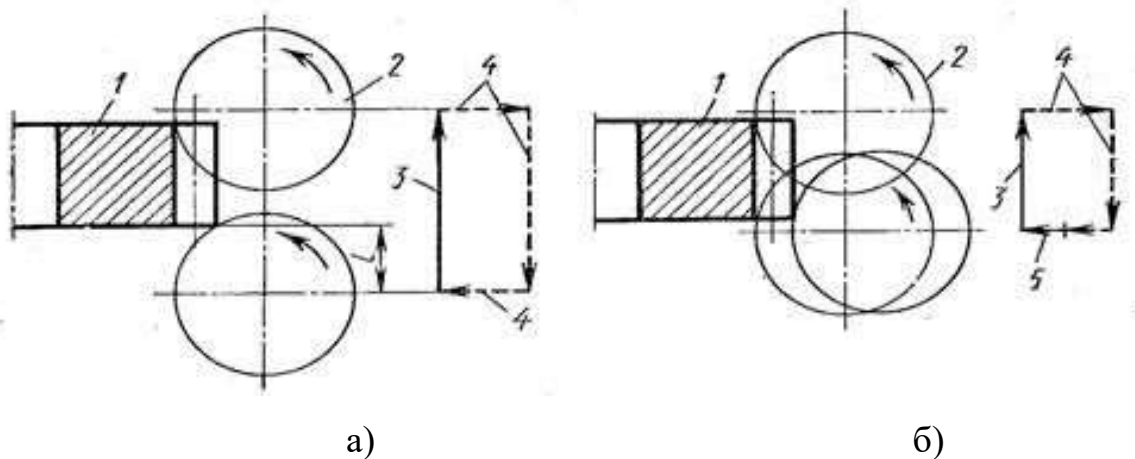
Схема нарізування зубів черв'ячною фрезою: а – з осьовою подачею; б - з радіально-осьовою подачею.
